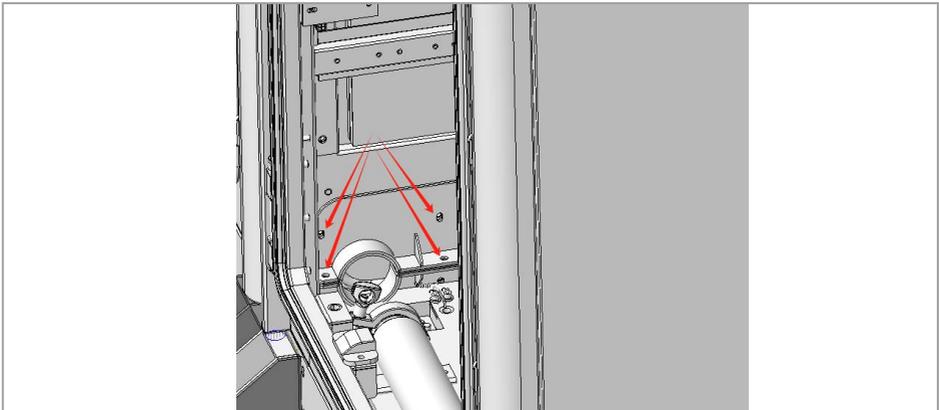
Entfernen der Schrauben der Dichtungsplatte
